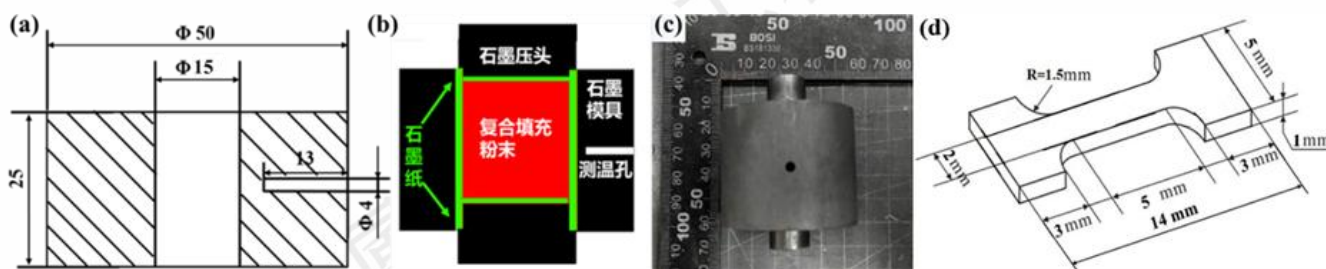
烧结模具及拉伸样尺寸及示意图: (a)烧结模具尺寸; (b)装配示意图; (c)实物图; (d) 拉伸样尺寸
